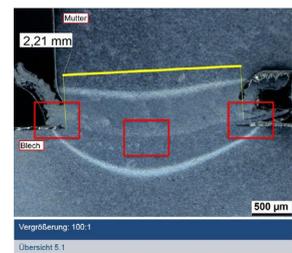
Schliffbild zur Bewertung einer Schweißung
